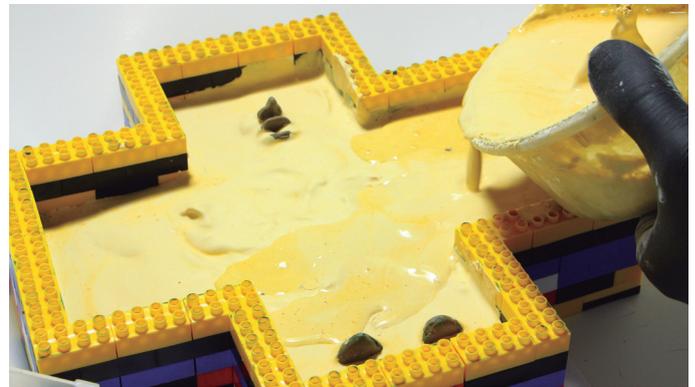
(a) Vaciado de yeso en la parte frontal del molde.
